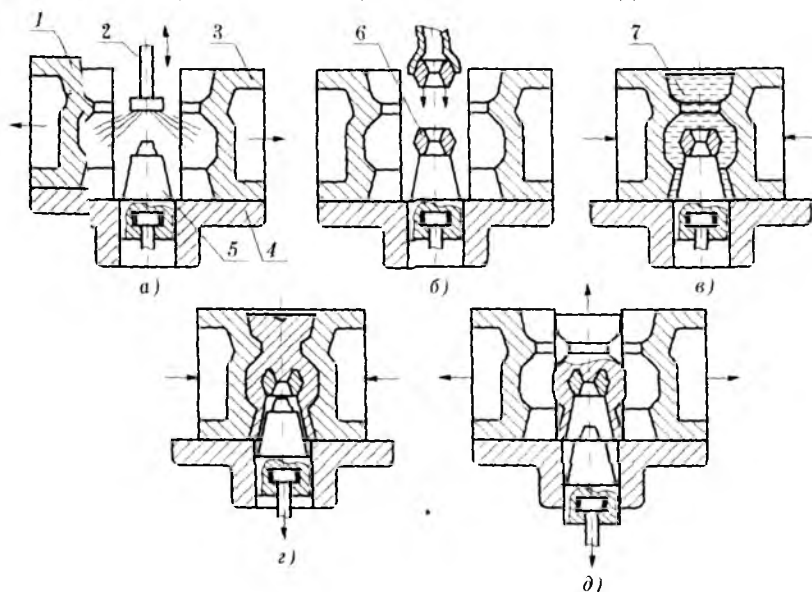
Схема изготовления отливки в металлической форме (кокиле):
